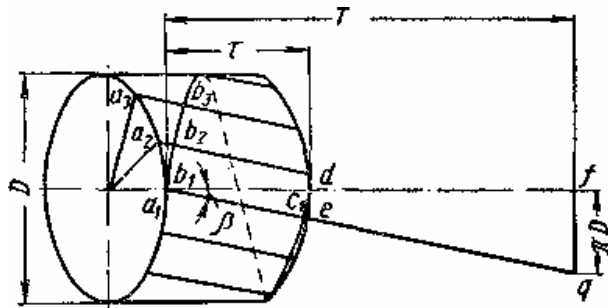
Схема определения числа зубьев, размещаемых на длине одного шага винтовой нарезки червячной фрезы
